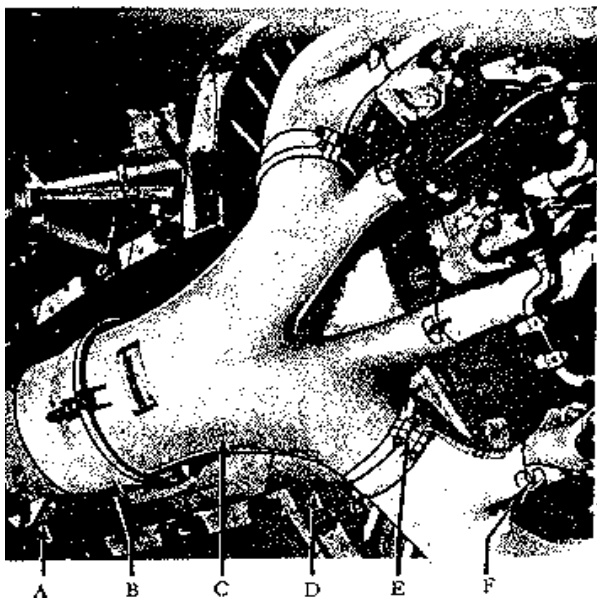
Vista explodida do conjunto de reforço do aquecedor pelo escapamento.
